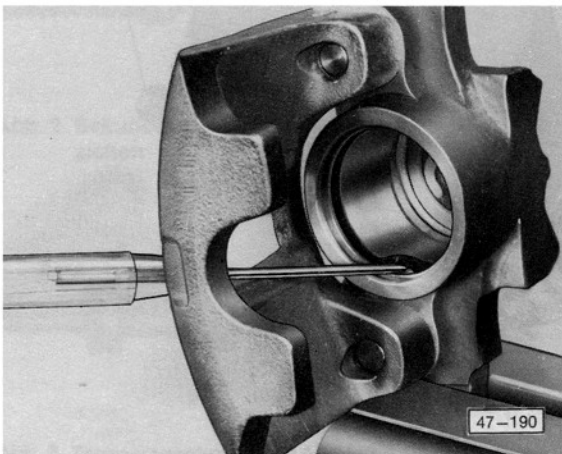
Dichtring vorsichtig mit einem Schraubenzieher herausnehmen
